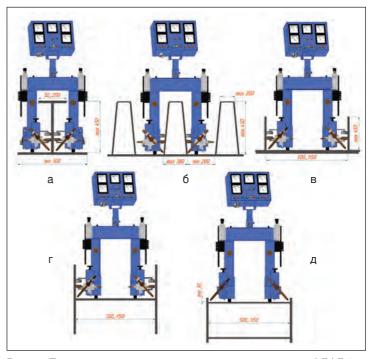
Примеры использования сварочного трактора АДФГ-502 ШТОРМ для сварки различных конструкций: а — сварка тавровых и двутавровых балок с вертикальным расположением стенки балки; б — сварка шпунтовых панелей; в — приварка ребер жесткости; г — сварка двутавровых балок с горизонтальным расположением стенки балки; д — сварка балок коробчатого сечения
